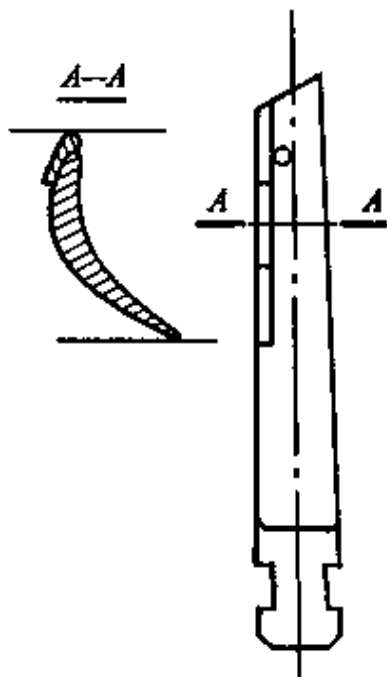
Рабочая лопатка со стеллитовыми накладками
